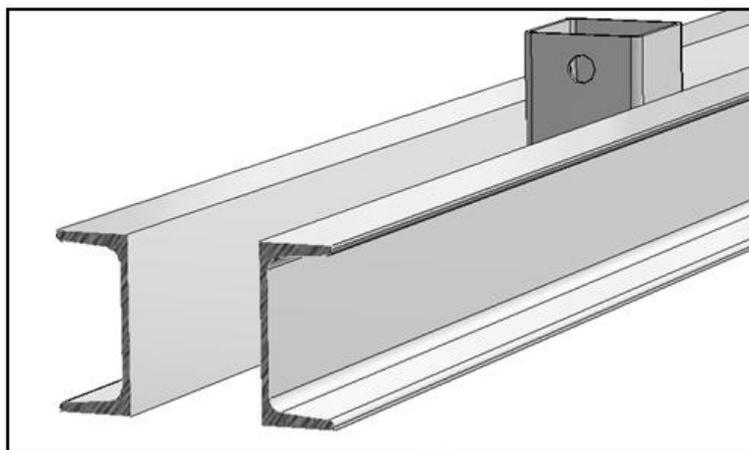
Assemblaggio dei profili a C con il tubolare per il supporto
